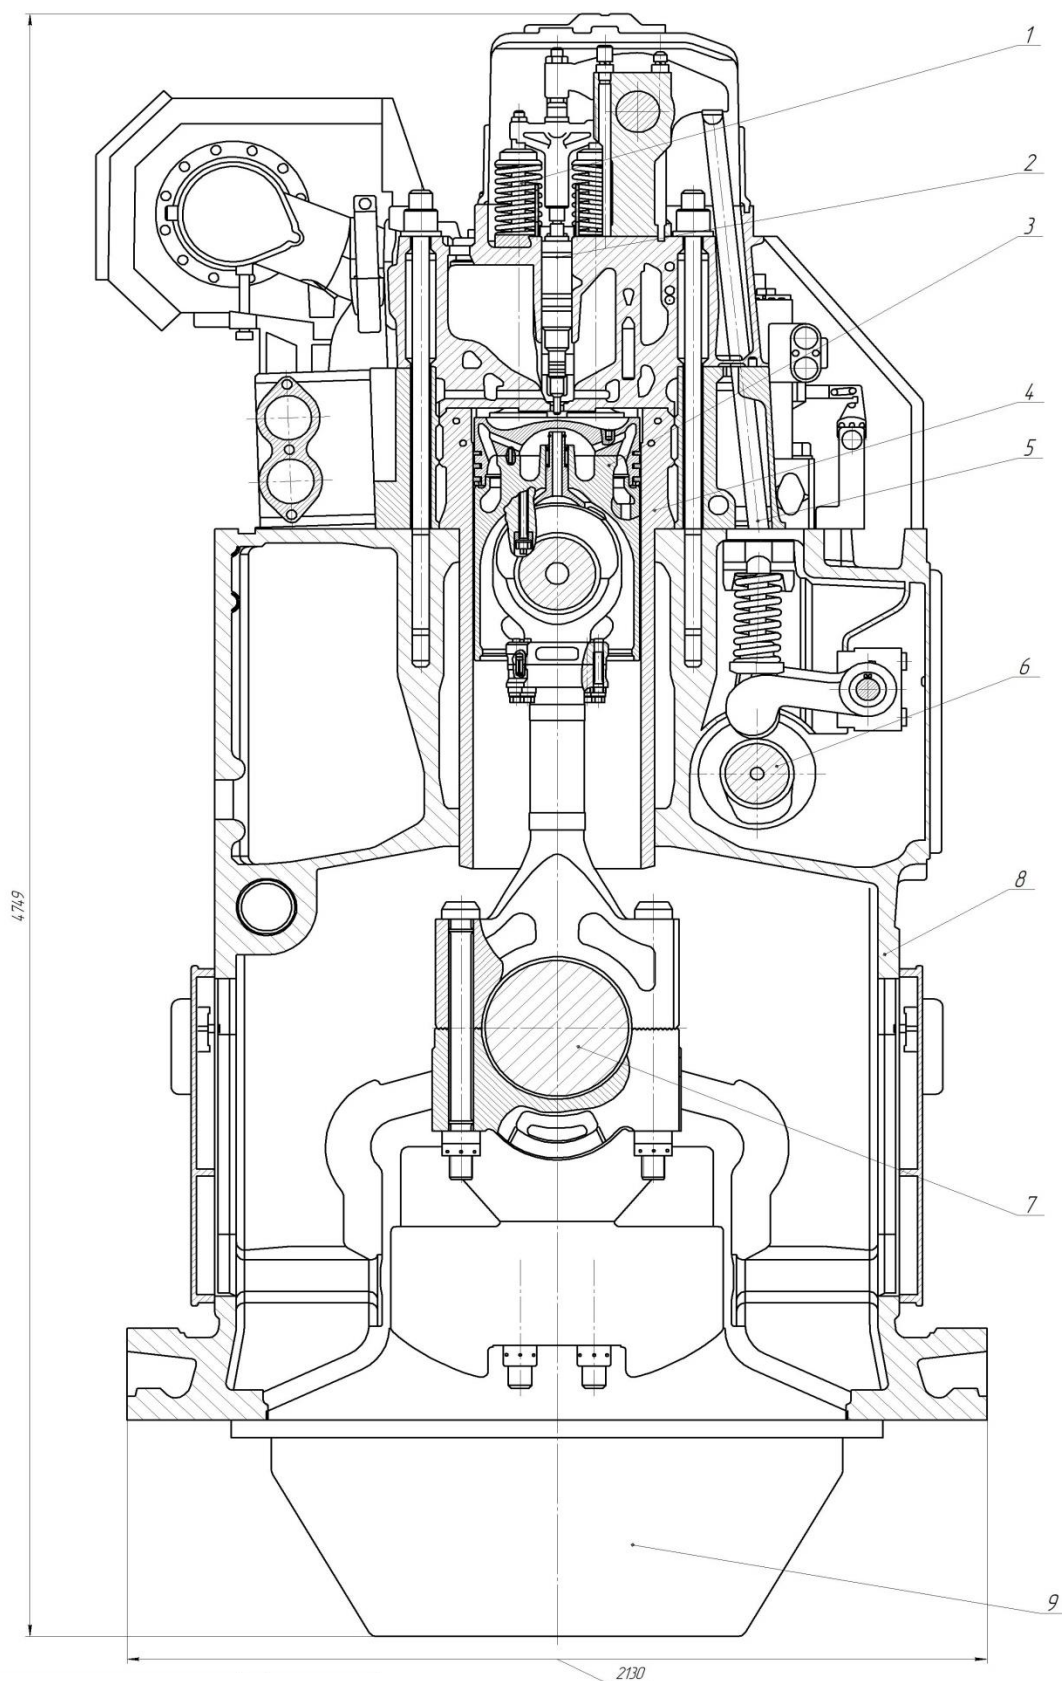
Поперечний переріз головного двигуна: 1 – клапан; 2 – паливна форсунка; 3 – поршень; 4 – циліндр; 5 – штовхач коромисла; 6 – шатун; 7 – колінчастий вал; 8 – блок-картер; 9 – піддон картера
